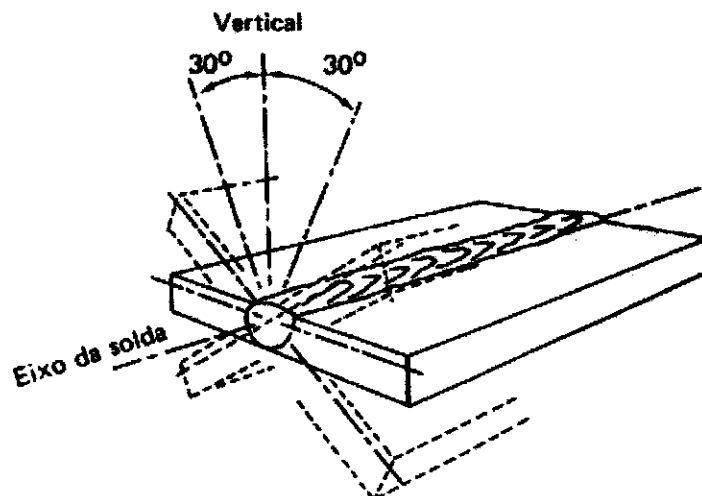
Soldagem na posição plana (FBTS, 1987).
